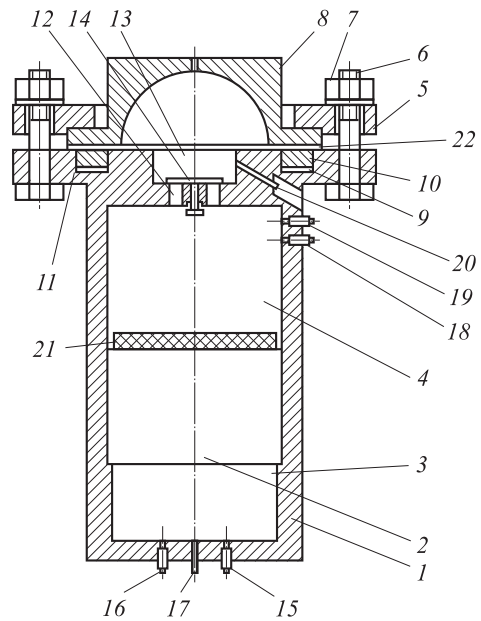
Схема двухкамерного устройства газовой штамповки:
